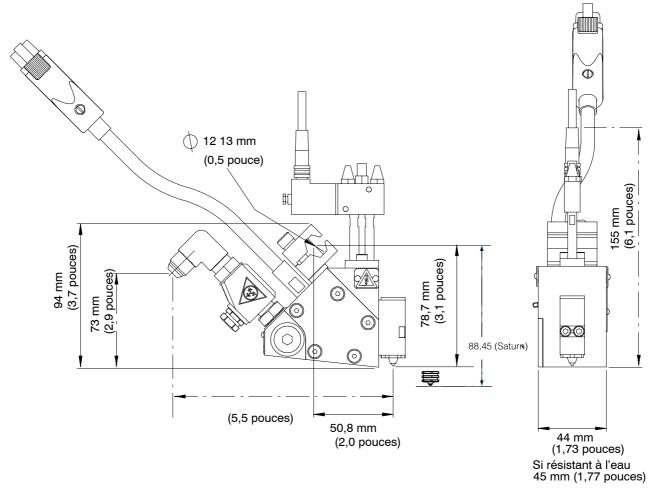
Dimensions d'un pistolet mono-module configurable à électrovanne SD
